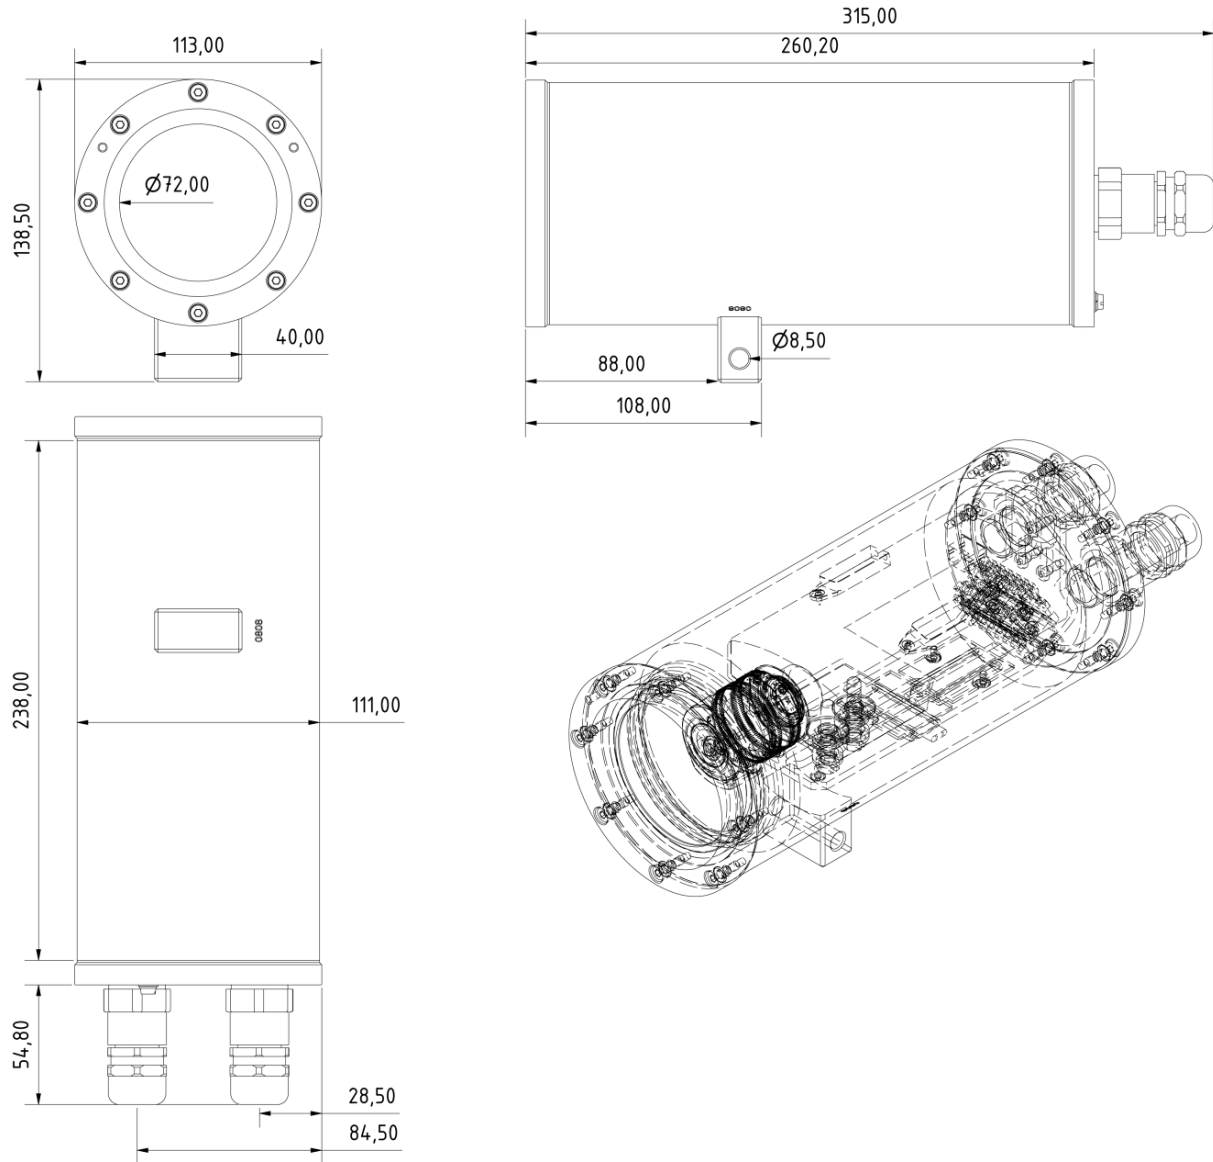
Abmessungen T08 ExCam IPQ1755 mit K1 Flansch
